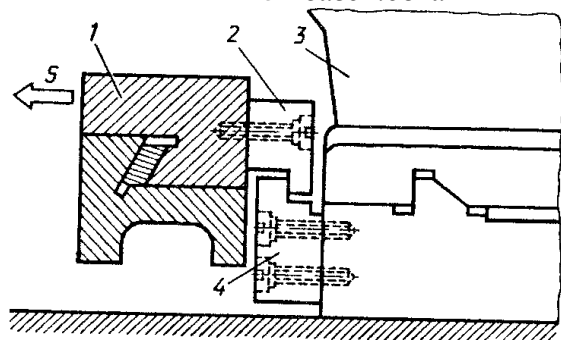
Схема прив'язування супорта до задньої бабки: 1 - поперечні полозки супорта; 2 - замок каретки супорта; 3 - задня бабка; 4 - замок задньої бабки
